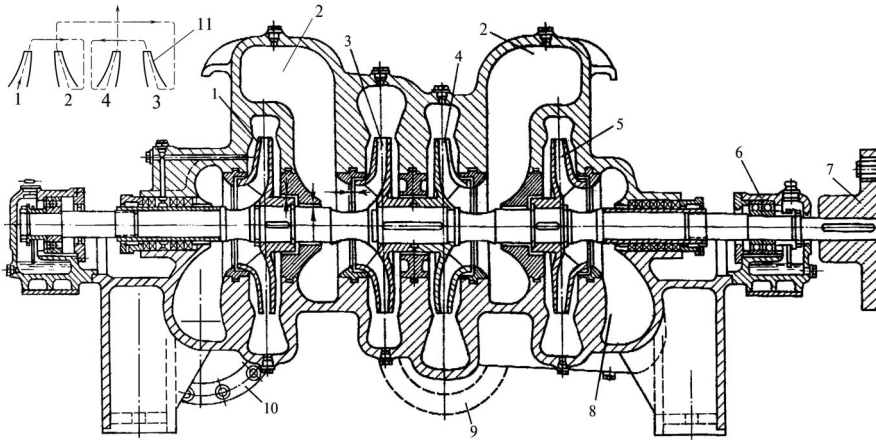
Поздовжній розріз відцентрового горизонтального багатоступеневого (чотириступеневого) насоса БС: 1, 3, 4, 5 - робочі колеса; 2 - лівий і правий перепускні канали; 6 - підшипник; 7 - напівмуфта; 8 - канал; 9 - напірний патрубок; 10 - усмоктувальний патрубок; 11 - схема руху рідини в насосі.
